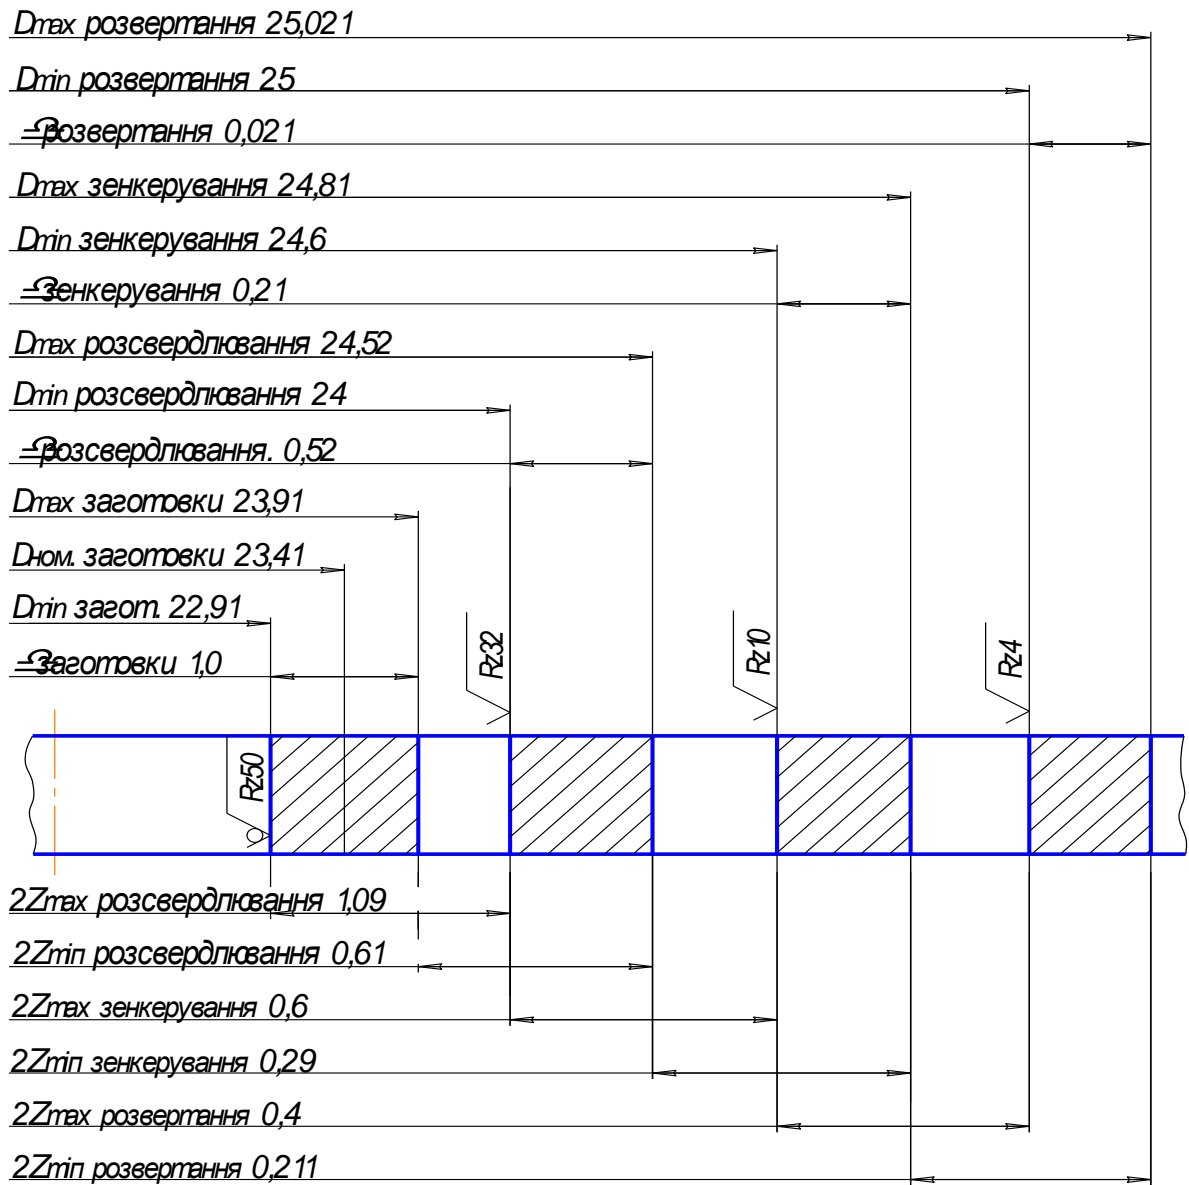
Схема розташування припусків та допусків для поверхні
